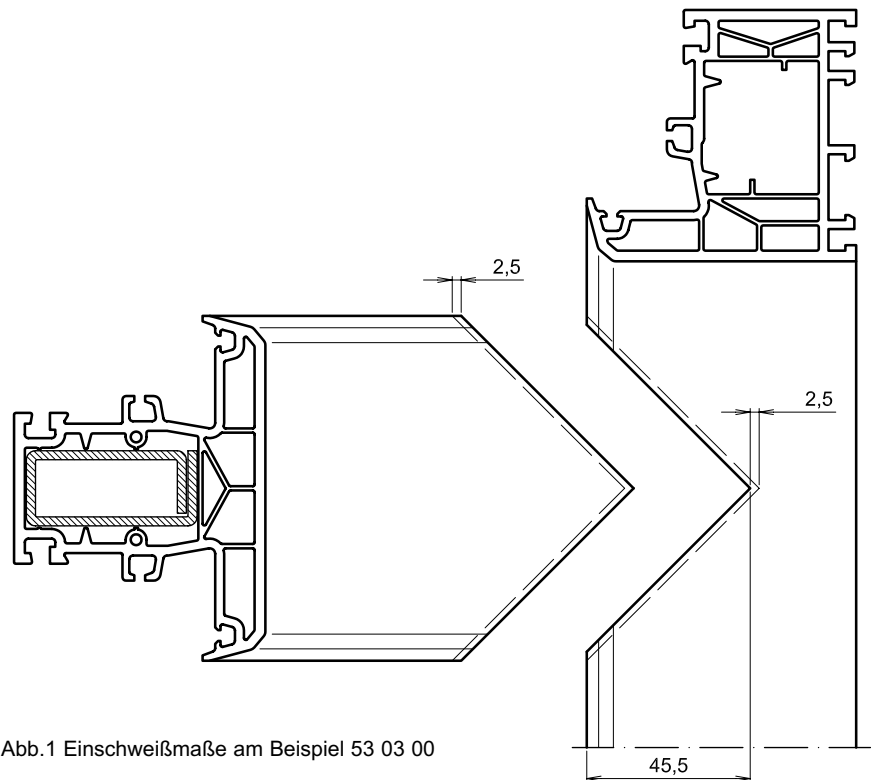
Einschweißmaße am Beispiel 53 03 00
